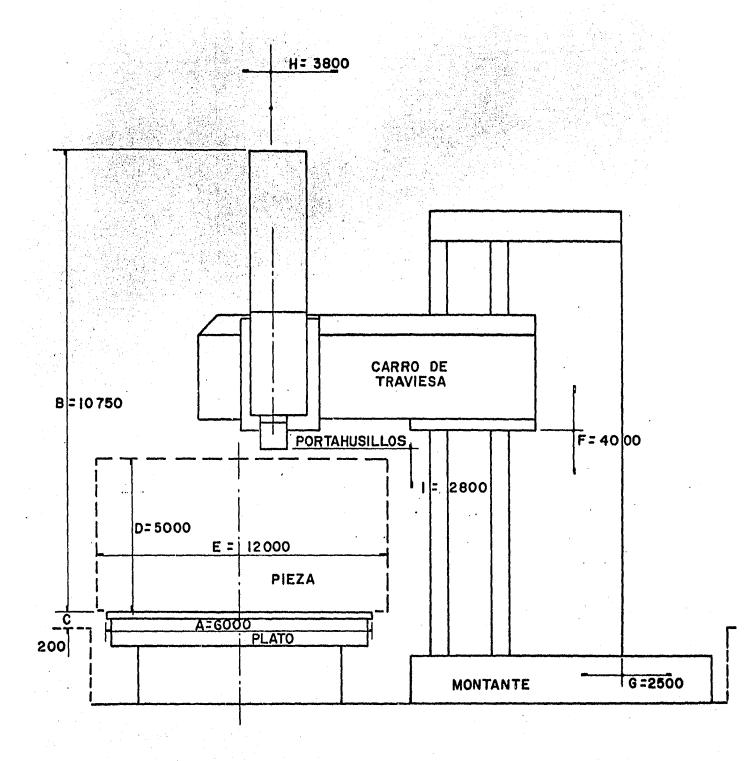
DIMENSIONES PRINCIPALES Y RECORRIDOS DE DESPLAZAMIENTO.
